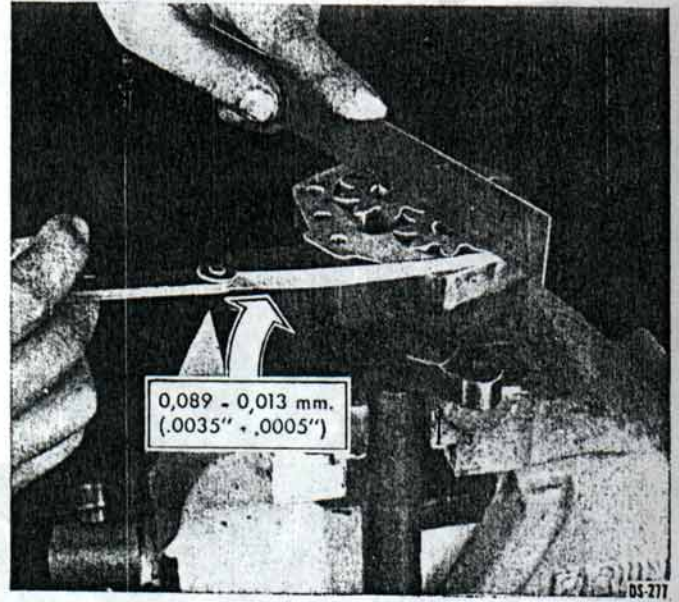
Verificando el juego libre entre el cuerpo de la bomba y la cara del engranaje.
